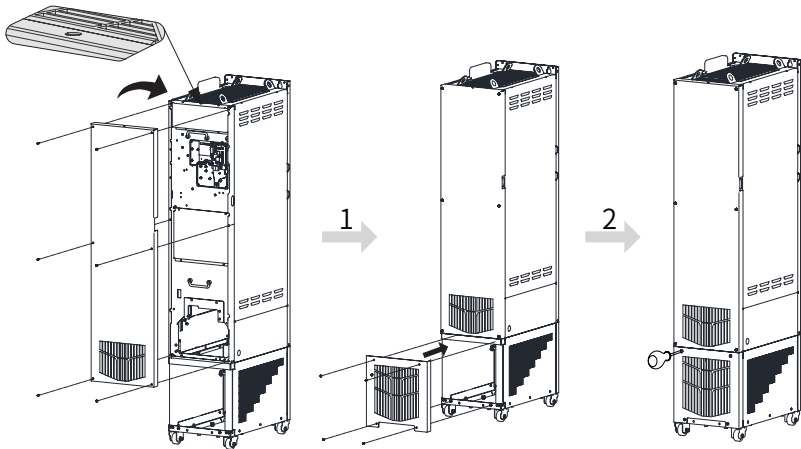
Установка крышек конструкций Т10 - Т12
